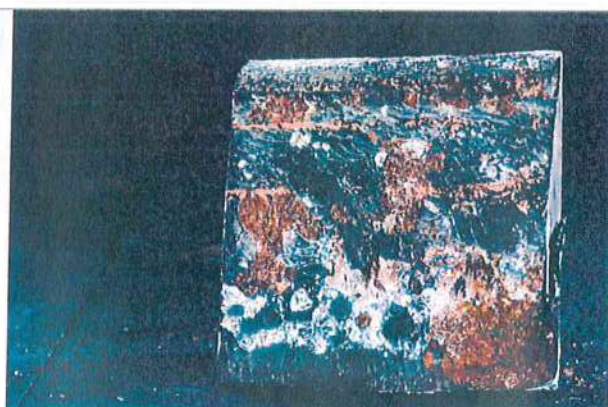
ASPETTO SUPERFICIALE DEL CAMPIONE
